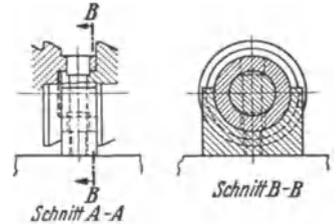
Befestigung der Schneideteile durch Spannkeil.
